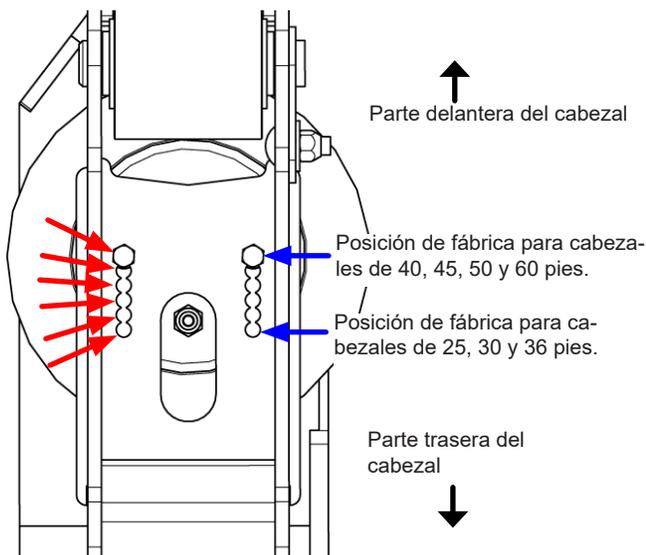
Posiciones de la bolsa de aire del bastidor auxiliar (se muestra la parte superior de la bolsa de aire)
